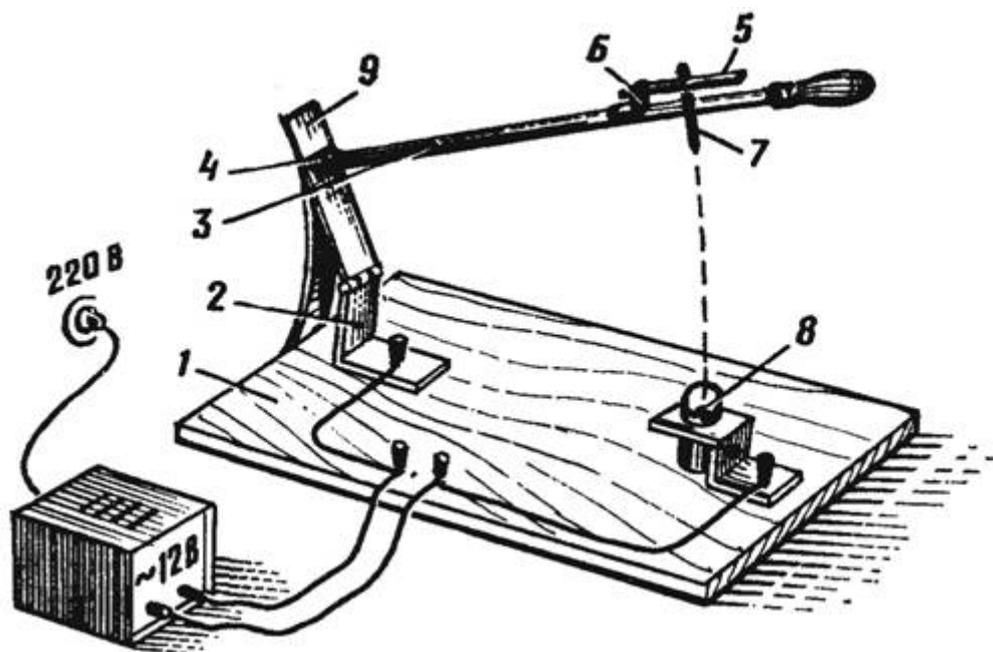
Приспособление для напайки вольфрамовых контактов.
